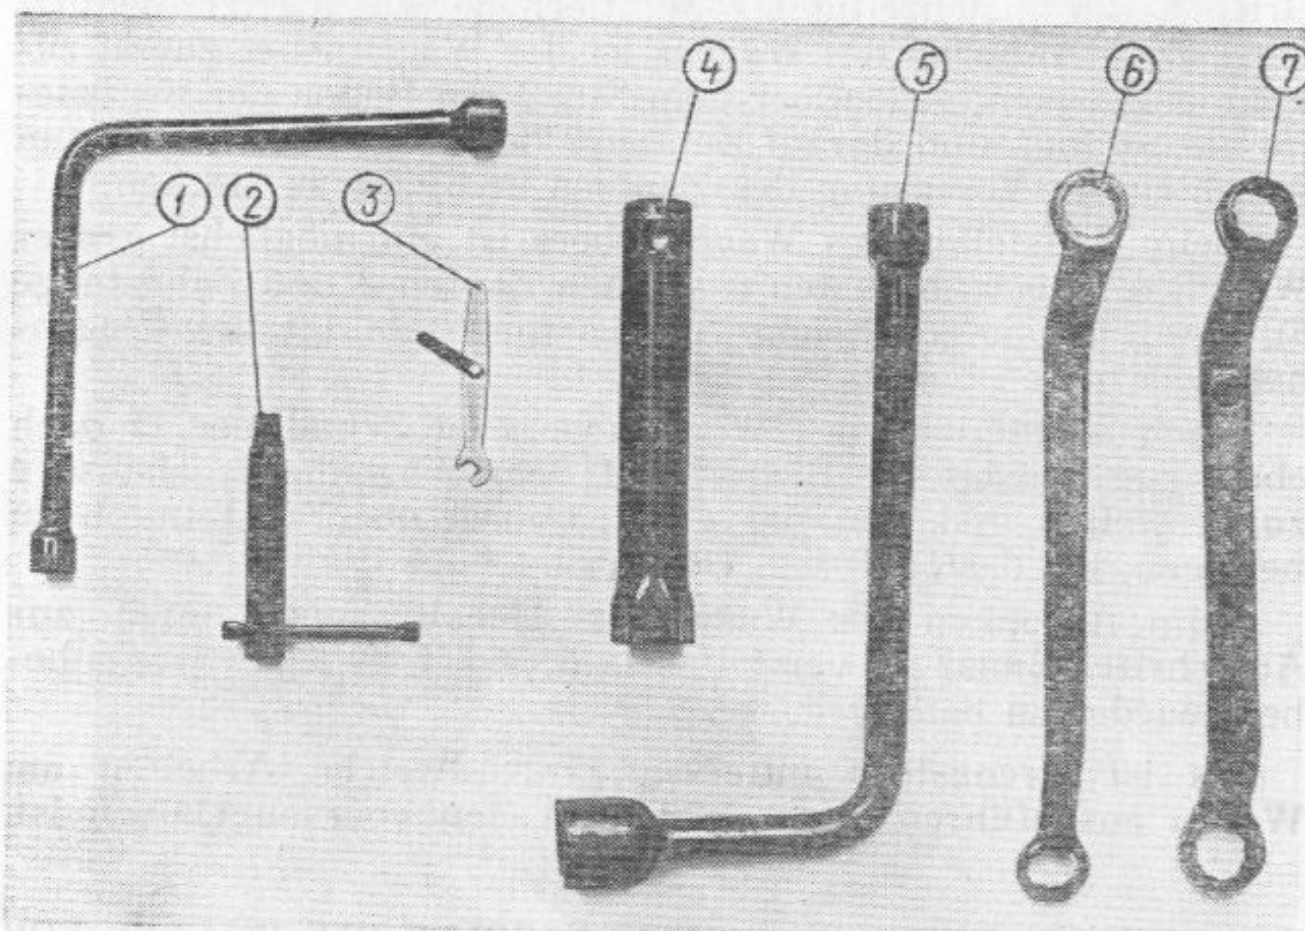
Spezialschlüssel, die dem Werkzeugsatz des Wagens mitgeliefert werden :
